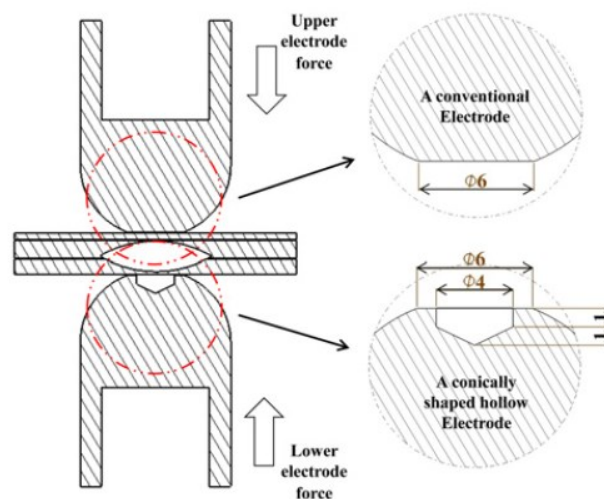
Géométrie et dimensions des deux électrodes dissymétriques utilisées par Kim *et al.* [44].
